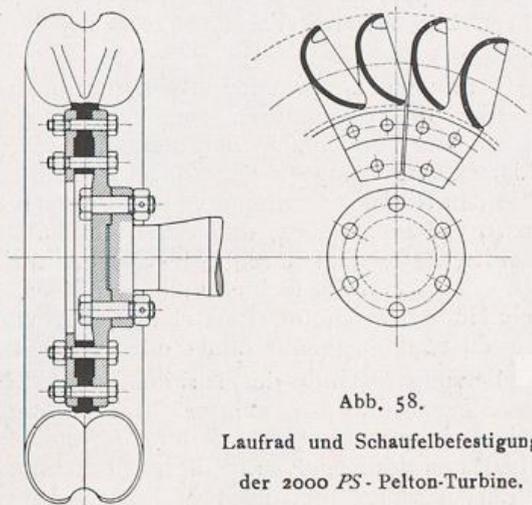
Laufrad und Schaufelbefestigung der 2000 PS-Pelton-Turbine.
